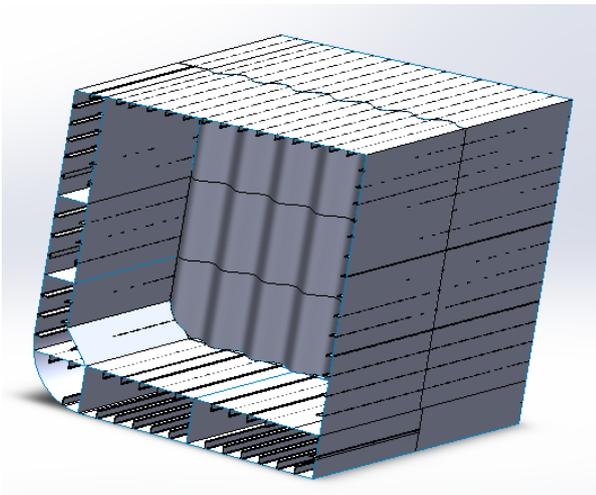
Sinusoid Corrugated Bulkhead Dengan Panjang Elemen 1600
